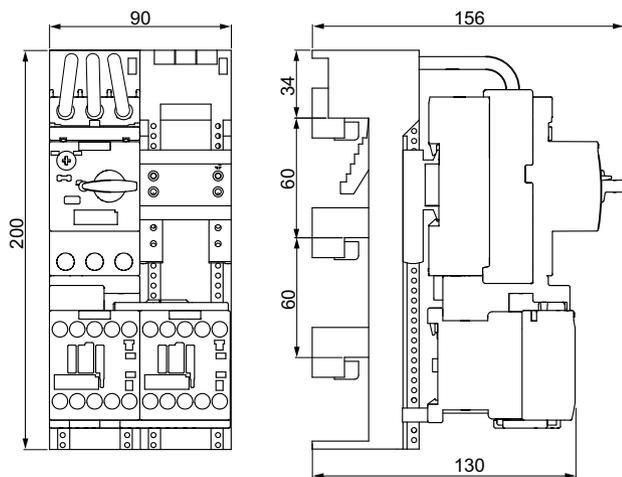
Arrancador inversor S00, AC/DC, bornes de tornillo
